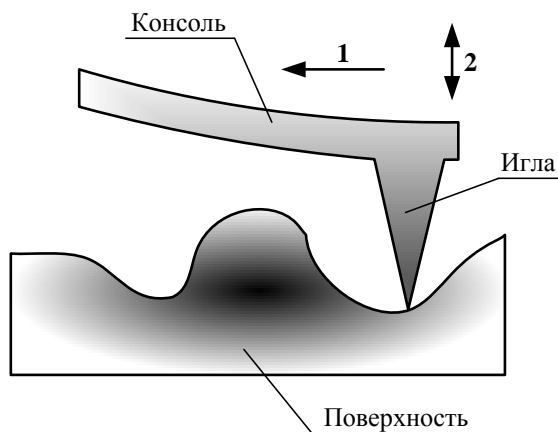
Контроль шероховатости поверхности контактным методом
